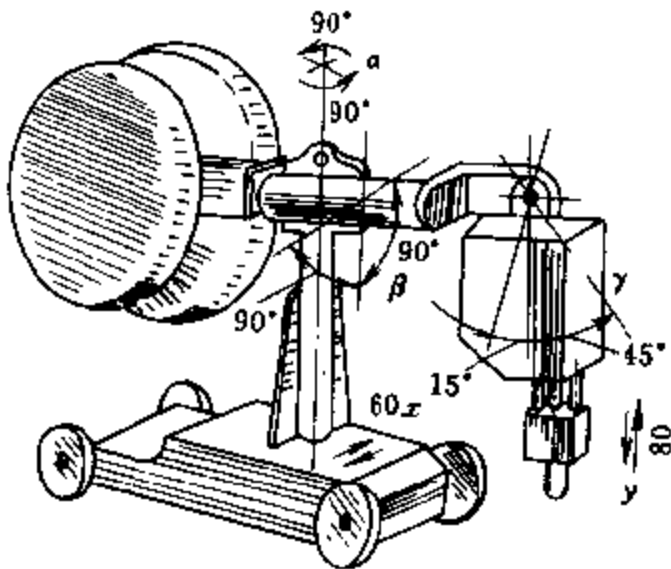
MZT-1000 型焊车可调部件示意图
